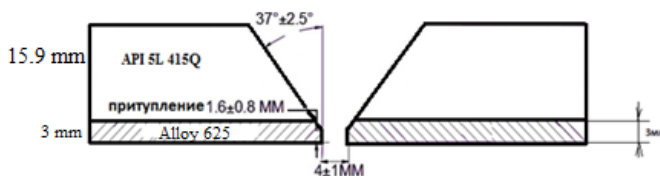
Разделка кромок под сварку плакированной трубы
